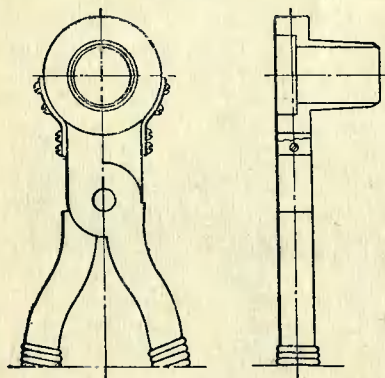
Клещи для сварки полихлорвиниловой муфты.
